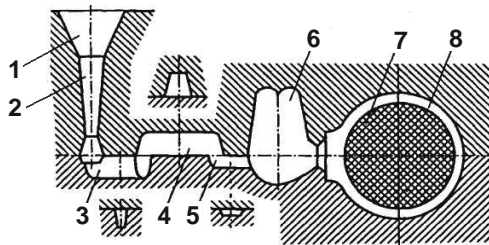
Схема ливарної форми: 1 – ливникова чаша; 2 – стояк; 3 – дросель; 4 – шлаковловлювач; 5 – живильник; 6 – бічний прибуток; 7 – стержень; 8 – робоча порожнина
